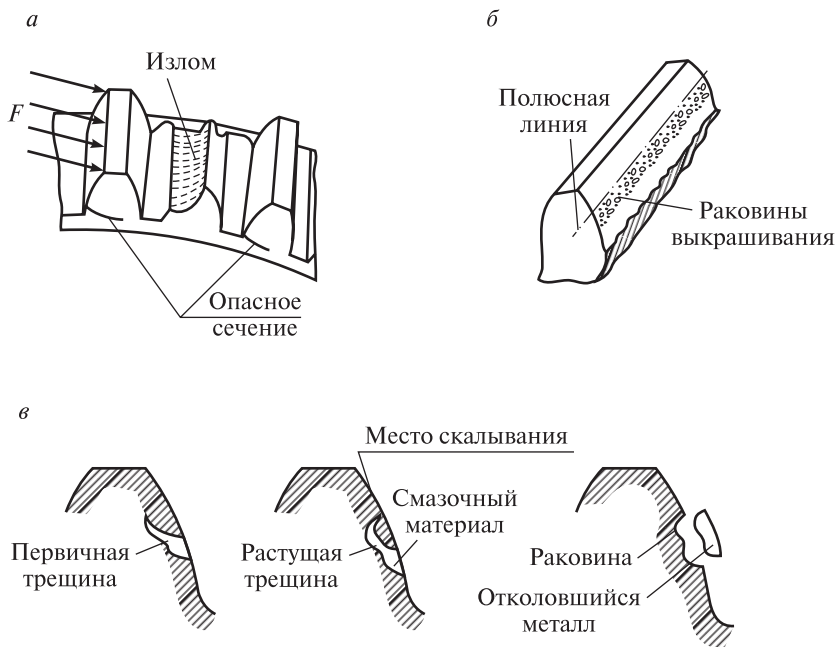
Виды разрушения зубьев цилиндрической прямозубой передачи:
